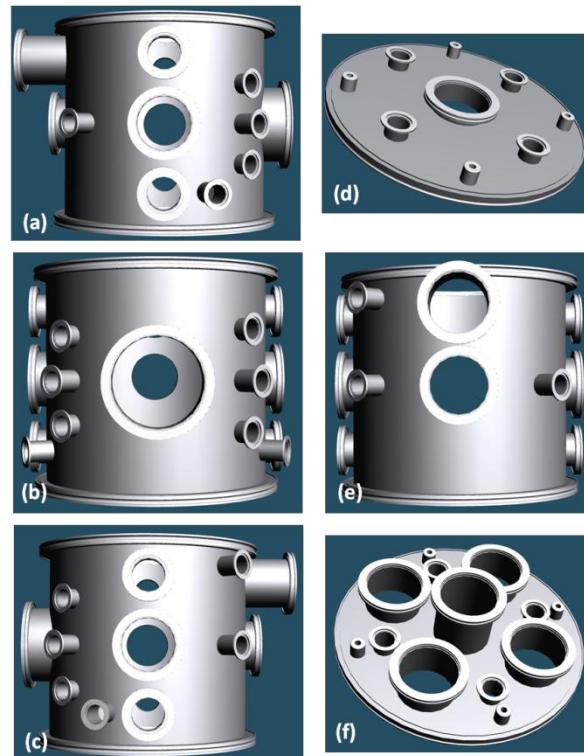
Schéma 3D du réacteur IDEFIX (a) vue de gauche ; (b) vue de face ; (c) vue de droite ; (d) vue de dessus ; (e) vue arrière ; (f) vue de dessous
